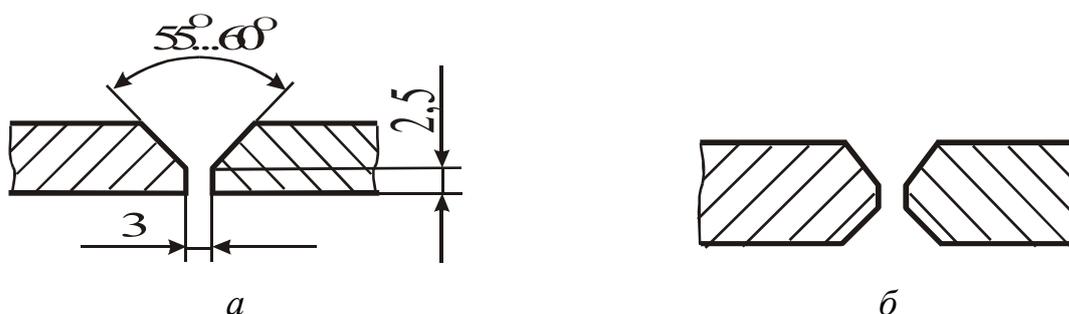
Підготовка кромки до зварювання: V-подібна (а) і X-подібна (б)
